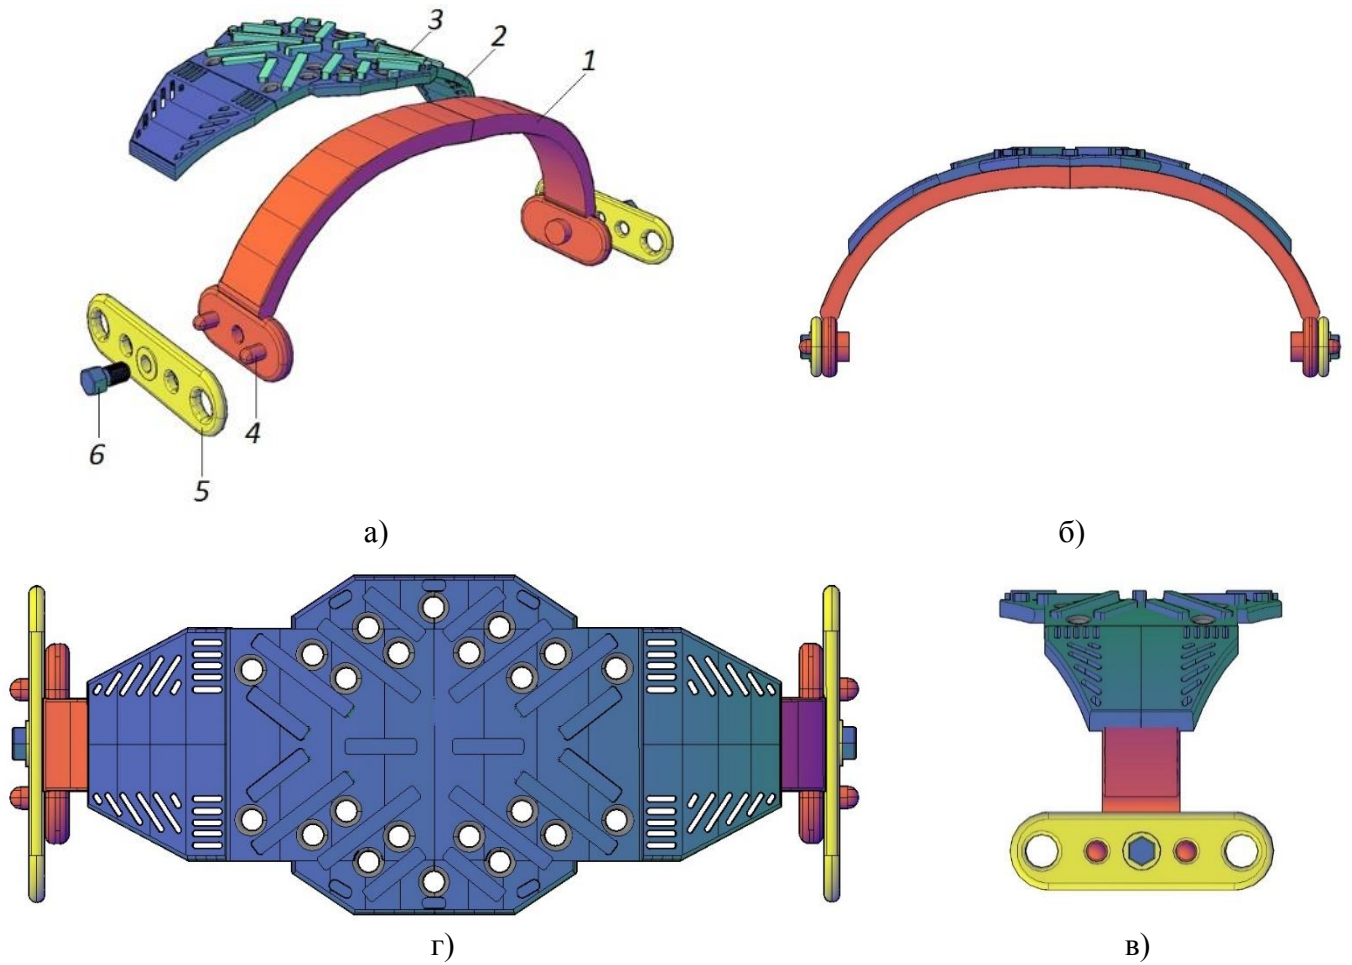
Конструкция трака: а – трак детализовка (1 – корпус; 2 – накладка перфорированная; 3 – грунтзацеп (протектора); 4 – ригель; 5 – соединительная пластина; 6 – винт); б – трак (главный вид); в – трак (вид сбоку); г – трак (вид сверху)
